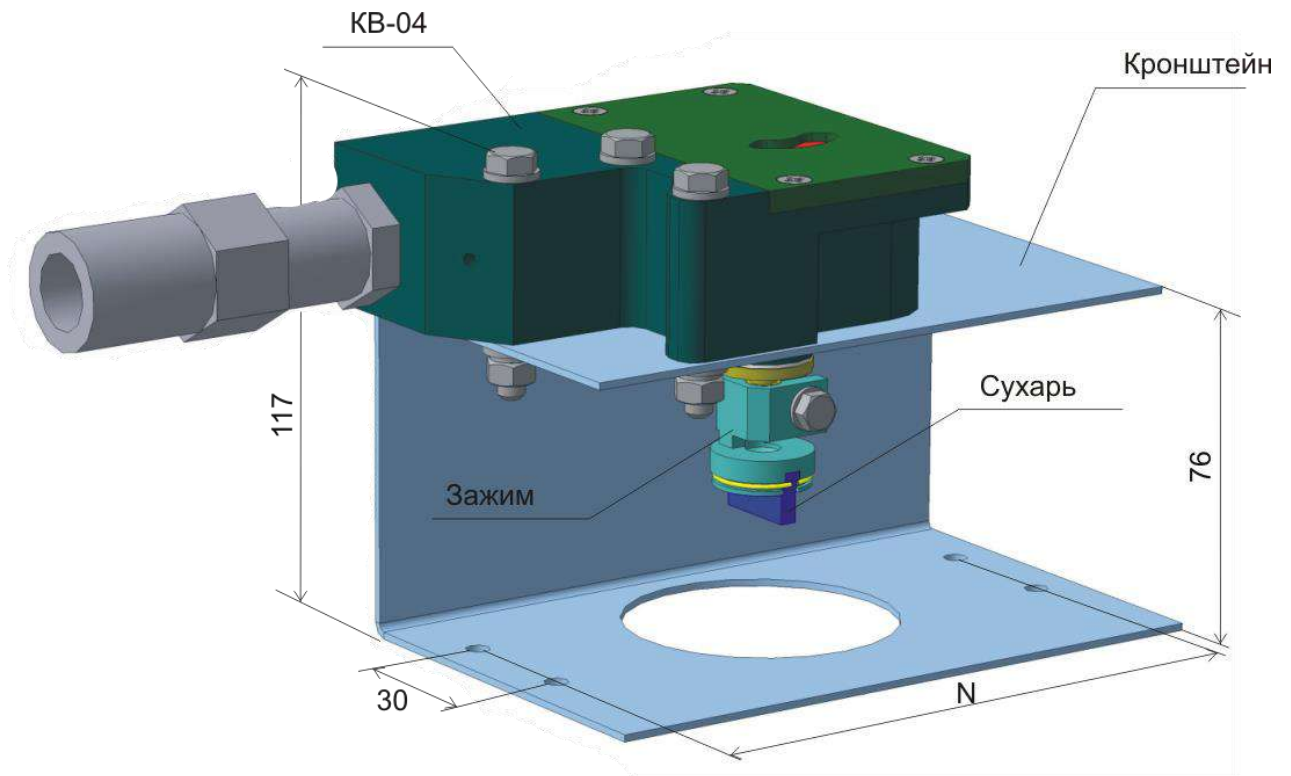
Монтажный чертеж выключателя KV-04
